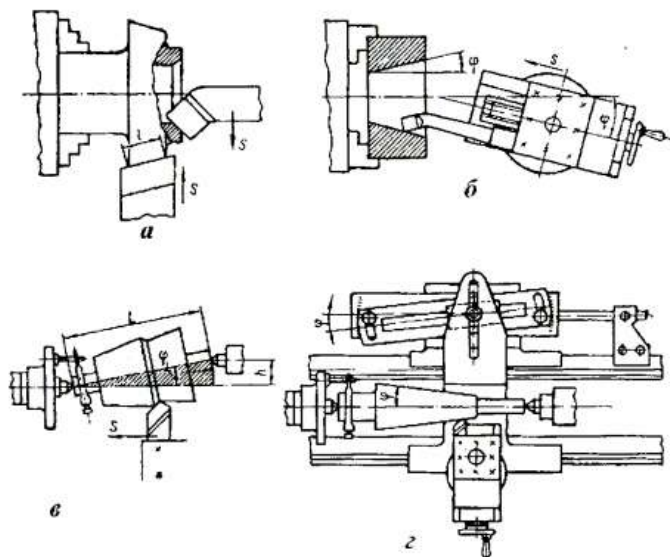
Схеми обробки конічних поверхнь різцями
